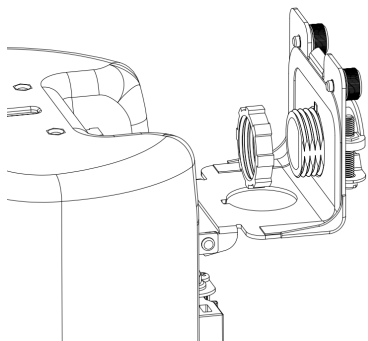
Mueve el pasacables hacia la parte superior y bloquealo.
